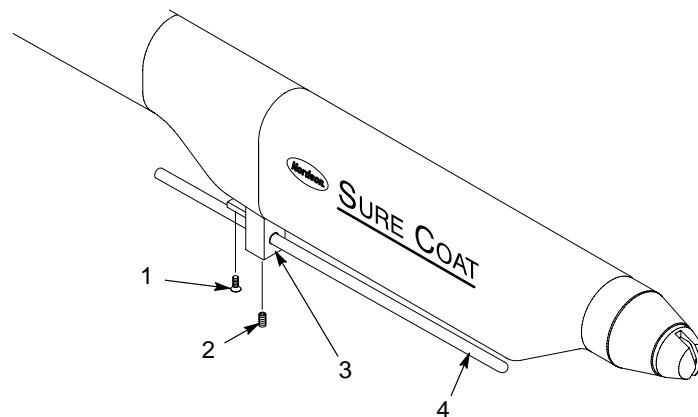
Kit de colector de iões para pistola com tubo de suporte
